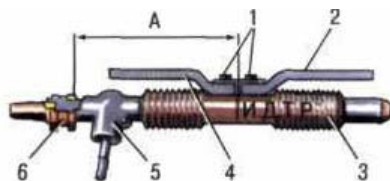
Нейтральное положение рейки, соответствующее прямолинейному движению автомобиля: 1 - болты крепления рулевых тяг; 2 - правая рулевая тяга; 3 - кожух картера рулевого механизма; 4 - левая рулевая тяга; 5 - картер рулевого механизма; 6 - левая опора
